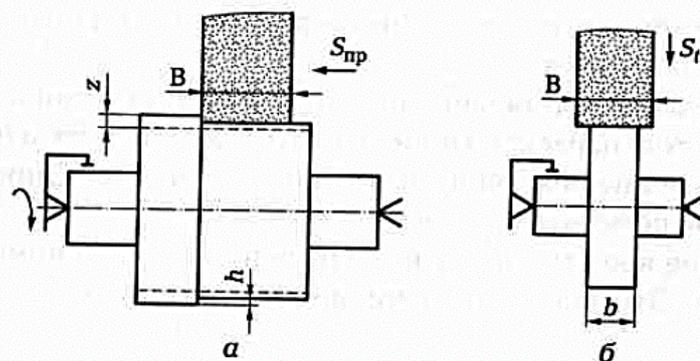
Шлифование наружной цилиндрической поверхности:
